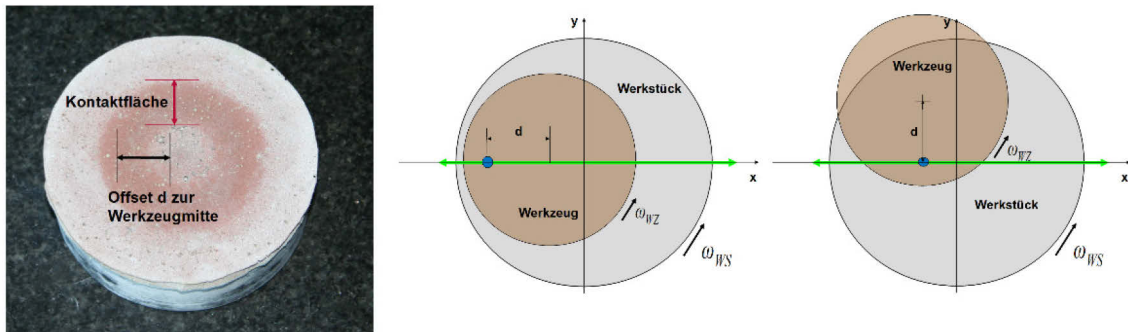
links: Werkzeug für die Offsetpolitur, die Kontaktfläche hebt sich dunkler auf dem Polierbelag ab, der Offset d zwischen Kontaktfläche und Drehachse ist in schwarz eingezeichnet; Mitte: Skizze von Werkzeug und Werkstück, Erzeugung des Offsets d parallel zur Werkzeugbahn; Rechts: Erzeugung des Offsets senkrecht zur Werkzeugbahn
